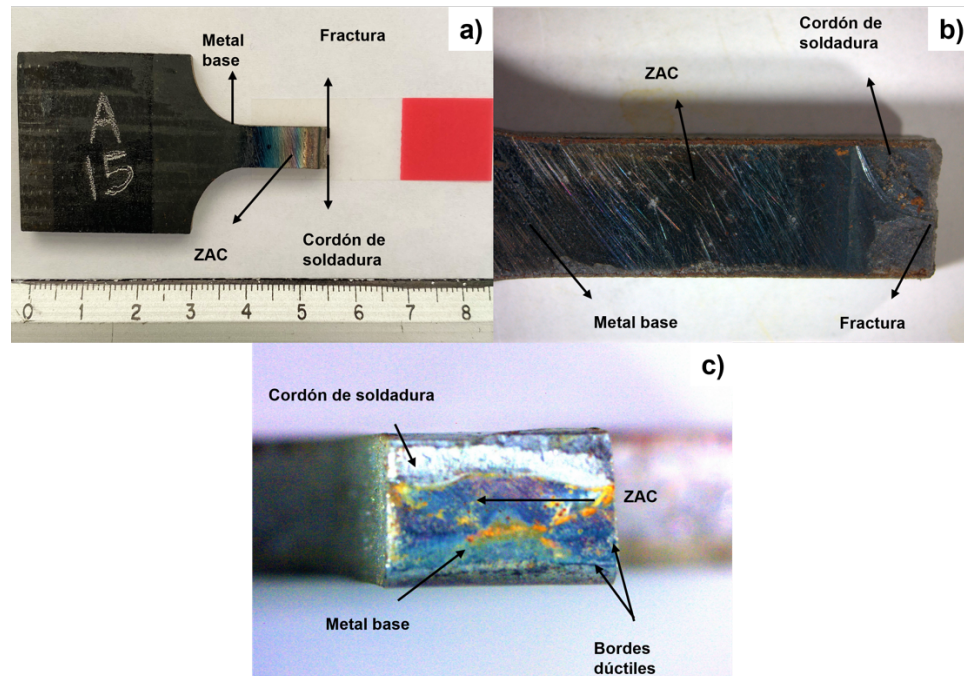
Fractografía de unión GTAW15 donde a) macroscópicamente se observa de sección de agarre de la probeta a la fractura, b) a 6.5x de forma longitudinal se muestra la fractura en el límite del cordón de soldadura y metal base, c) transversalmente se observa fractura en el cordón con grieta en el límite de la penetración.
